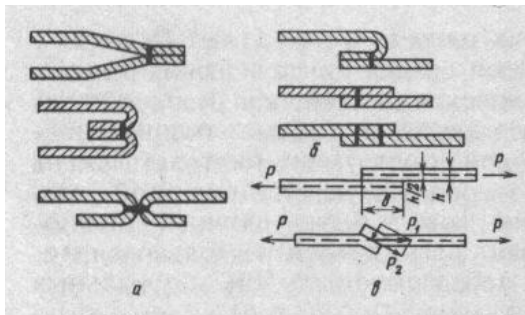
Сварные швы синтетических тканей, выполненные ультразвуковой сваркой (а – стачные; б – накладные) и схема испытания накладных сварных швов(в)
